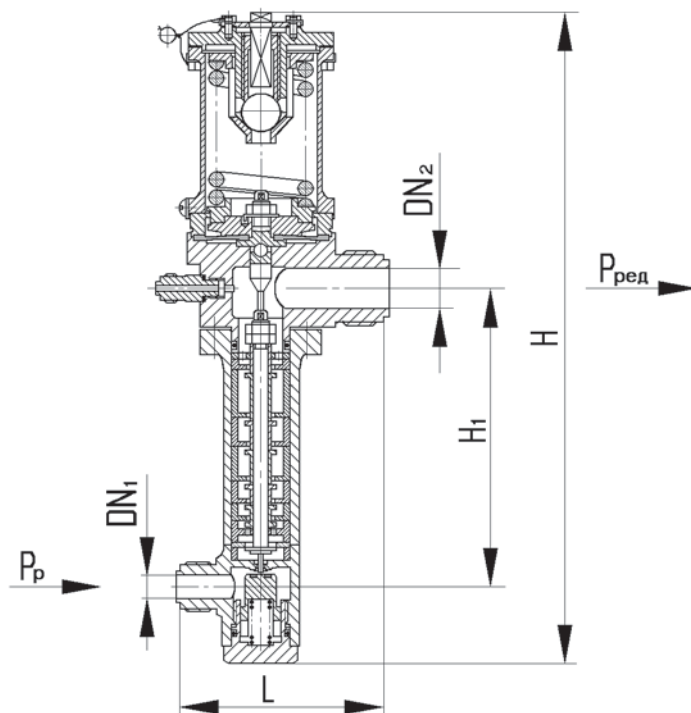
Клапан редукционный проходной штуцерный
